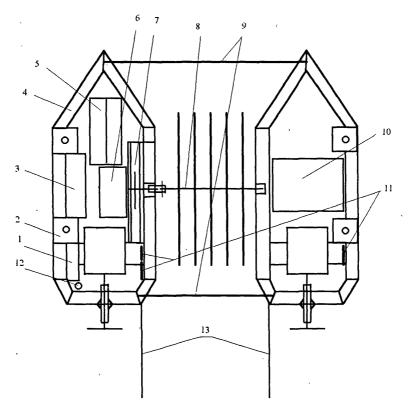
Вид сверху: 1 — корпус демодулятора; 2 — 4 рейки крепления вертикальных стяжек; 3 — корпус приемника; 4 — палубные рейки; 5 — 2 батареи 3R12; 6 — двигатель редуктора; 7 — редуктор; 8 — барабан; 9 — стяжные рейки; 10 — аккумулятор; 11 — УПТ двигателей; 12 — антенна; 13 — шечки
